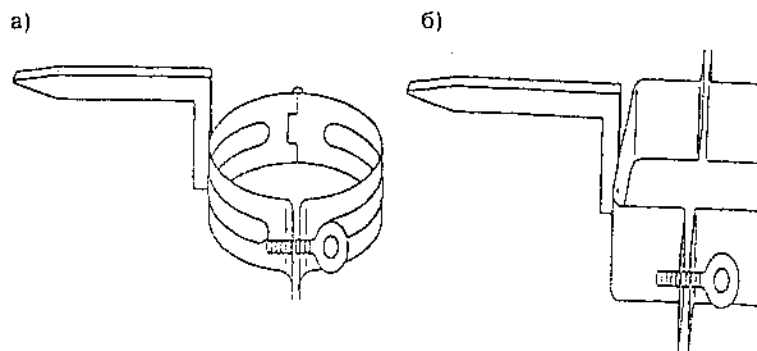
Крепежный кронштейн для круглой (а) и коробчатой (б) труб
